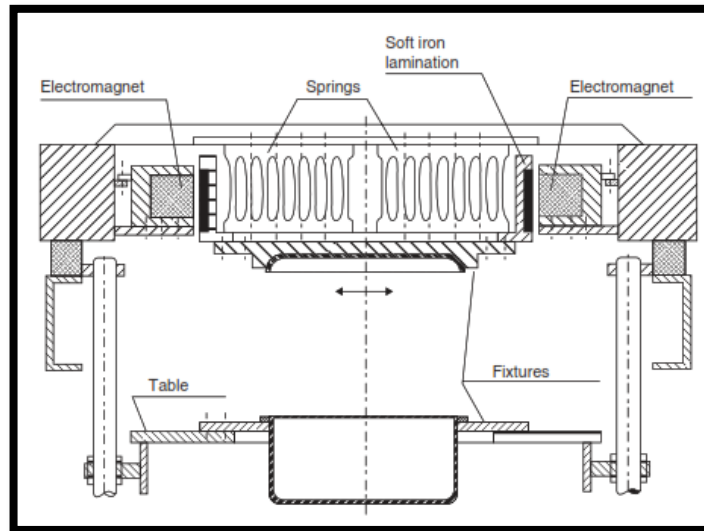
Una máquina de soldadura por fricción lineal típica
